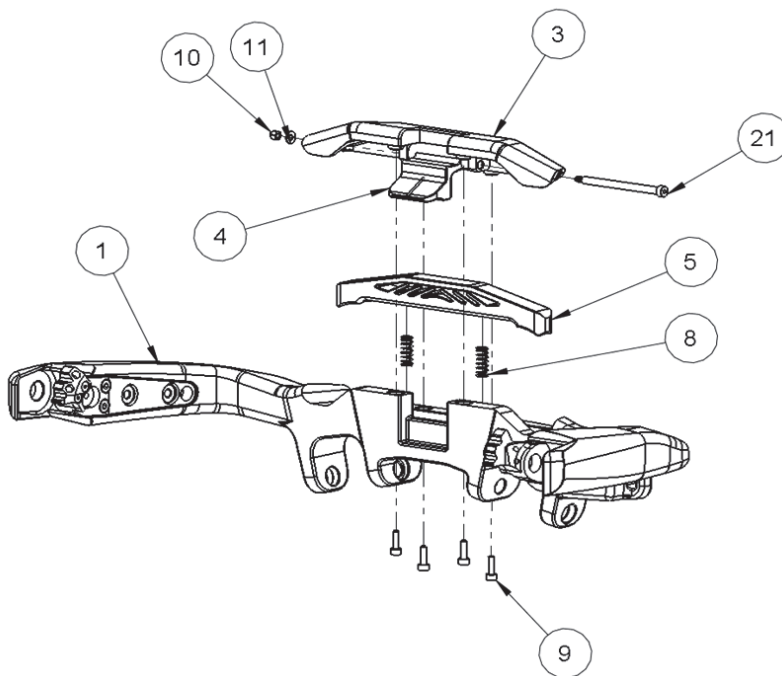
Vista explodida do conjunto traseiro — parte 1
